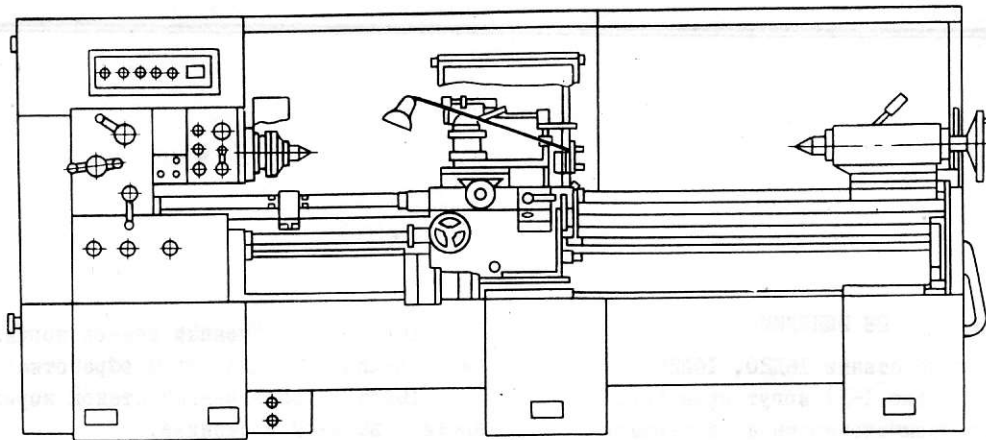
Станок токарно-винторезный I6D25 с длиной обработки L = 2000 мм
